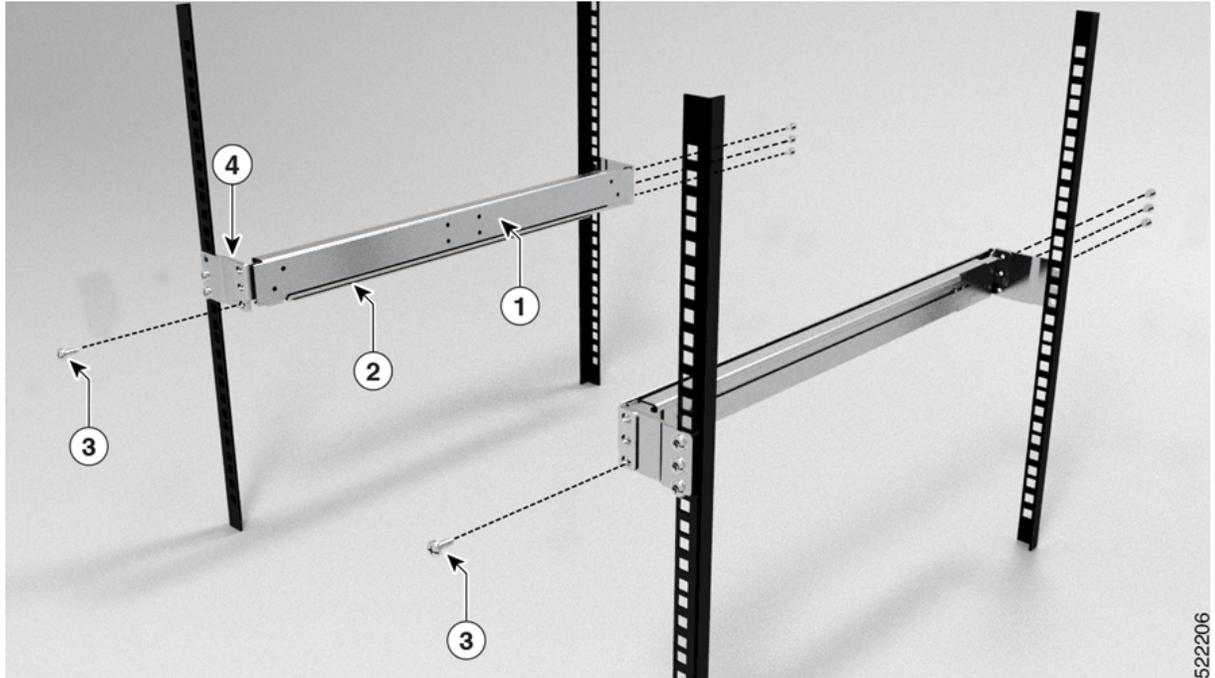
Assemblage du rail coulissant pour montage sur un rack de 19 pouces à 4 montants
